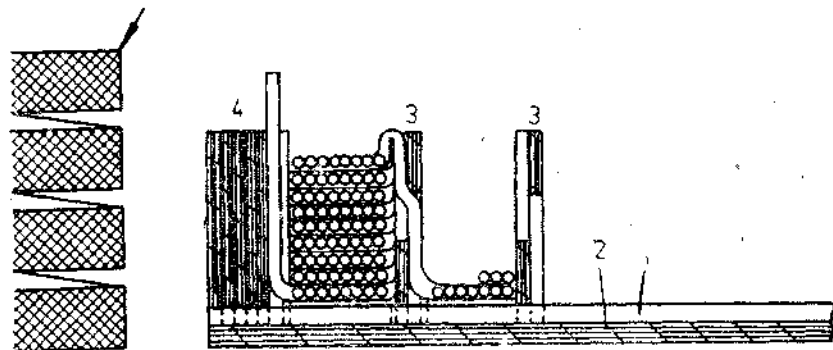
Înfășurarea în galeți depănați în același sens (galeți simpli):
